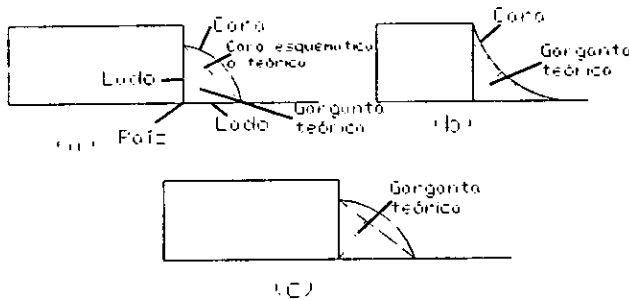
(a) Superficie convexa. (b) Superficie cóncava. (c) Soldadura de filete de lados desiguales.
